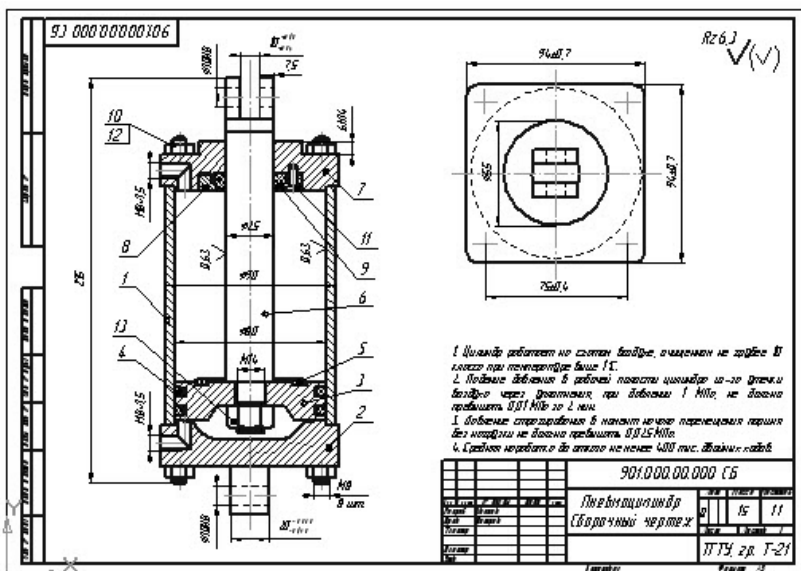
Сборочный чертёж пневмоцилиндра
